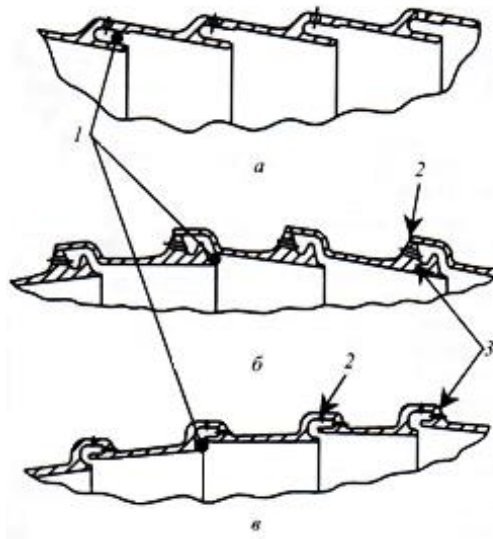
Пленочная система охлаждения из точеных секций: 1 – кольцевой канал; 2 – лазерная сварка; 3 – кольцевые ребра
